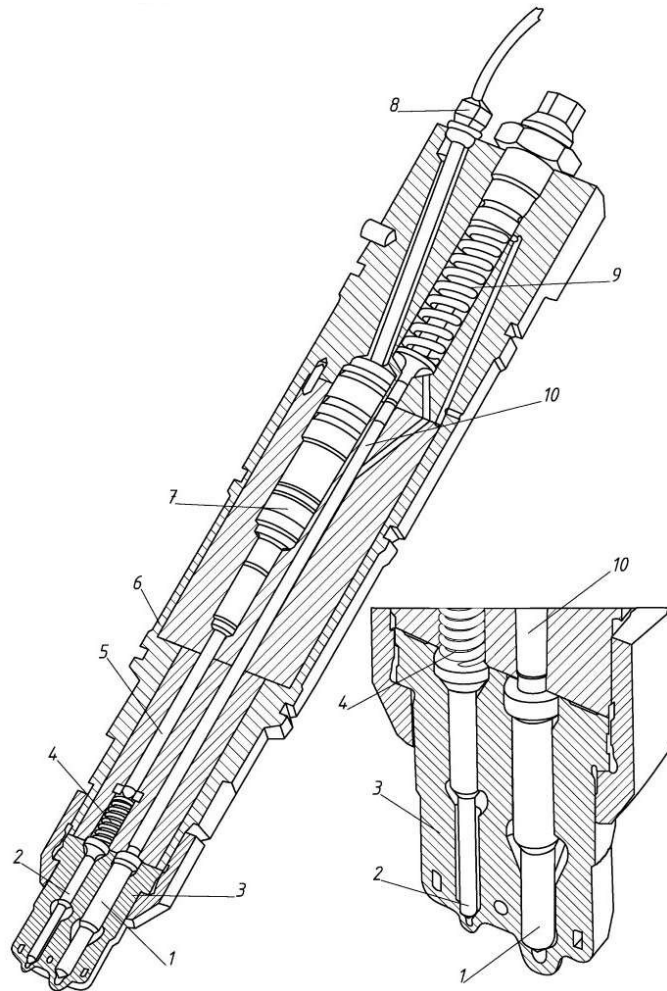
Форсунка газодизельного двигуна 50DF фірми Wärtsilä зі здвоєним розпилювачем для резервного і запального рідкого палива:
